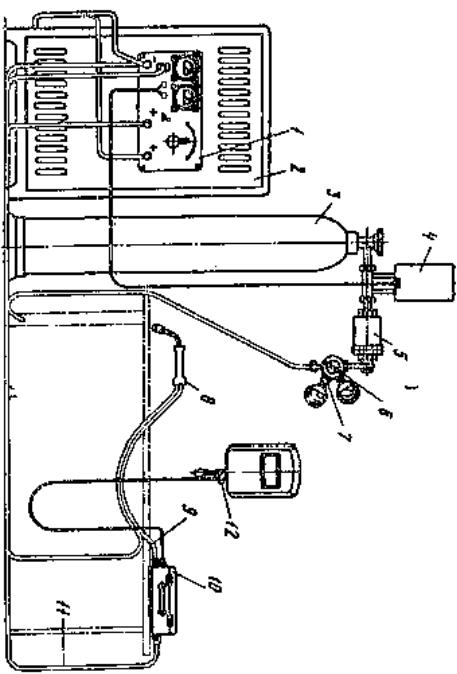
Общая схема установки полуавтомата А-547У для сварки в защитном газе:
